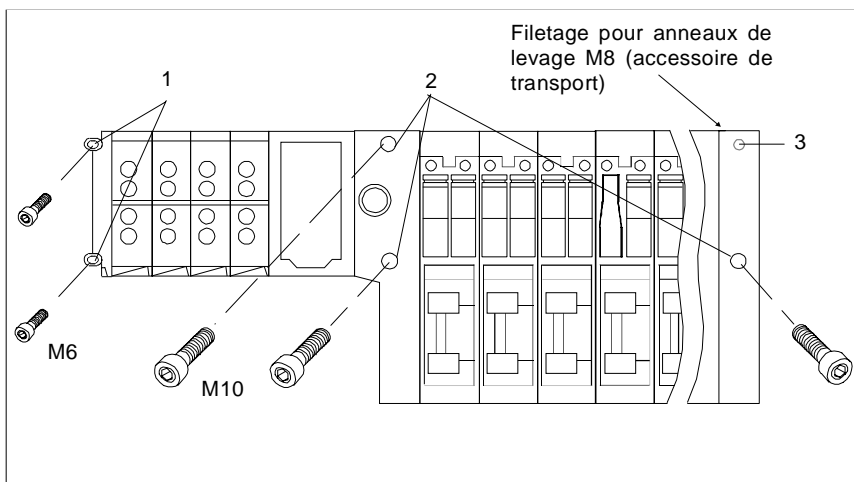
/6 : Montage sur panneau d'un terminal ISO type 05
